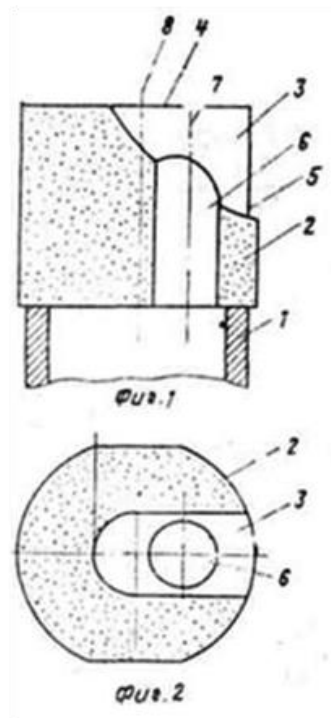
конструкція алмазного свердла на металевій зв'язці.
